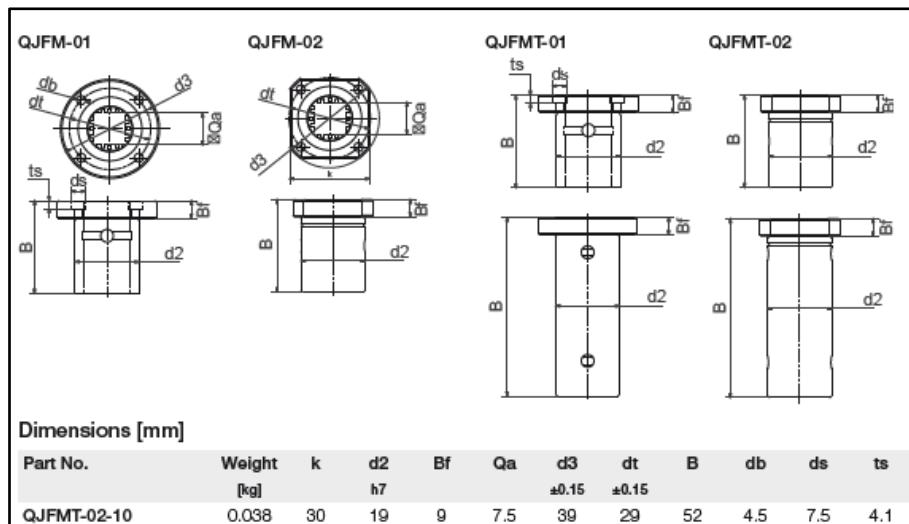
Especificações sobre a flange do sistema de guiamento linear
